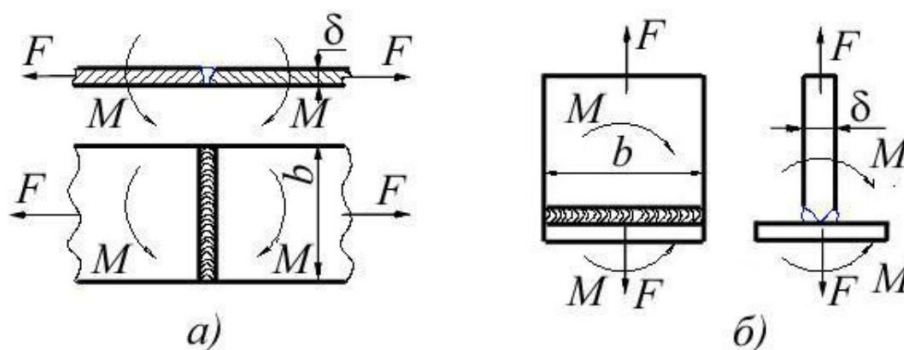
Сварные соединения со стыковыми швами: a – стыковое; b – тавровое с разделкой кромок
